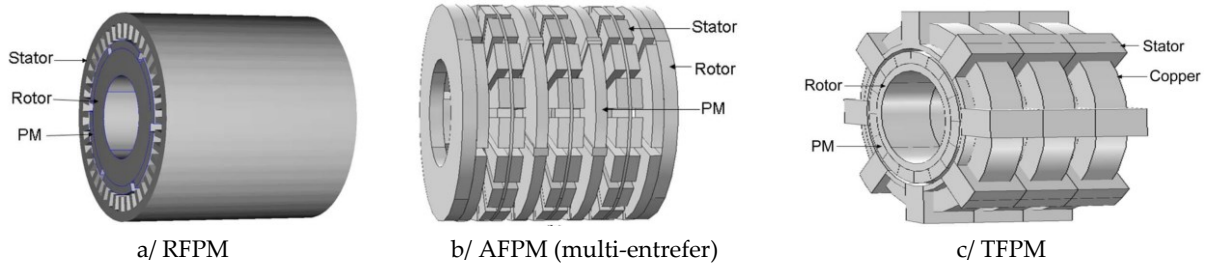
Catégories de machines en fonction de la direction principale du flux [83]
